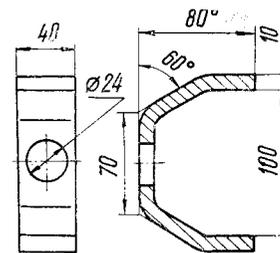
Скоба упорная приспособления для разборки муфты фрикционной привода вентилятора дизелей
